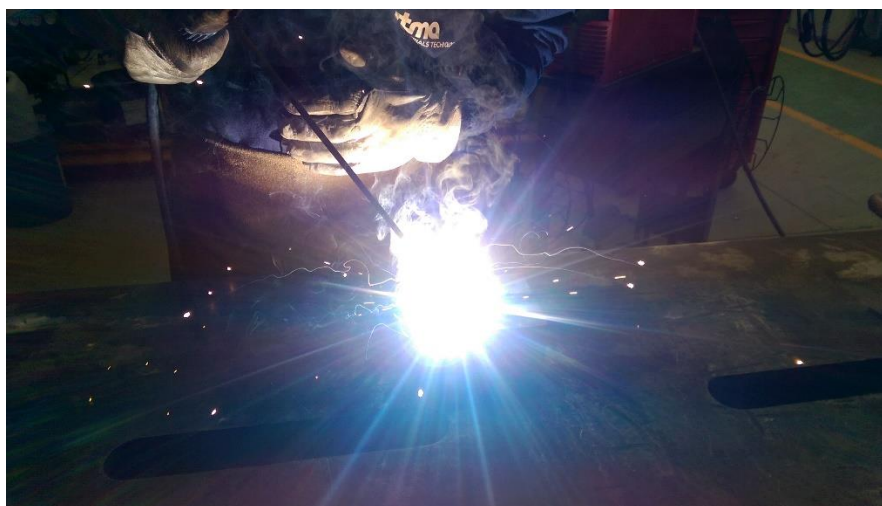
Pruebas de soldadura con electrodos revestidos en plantas piloto de soldadura de ITMA
